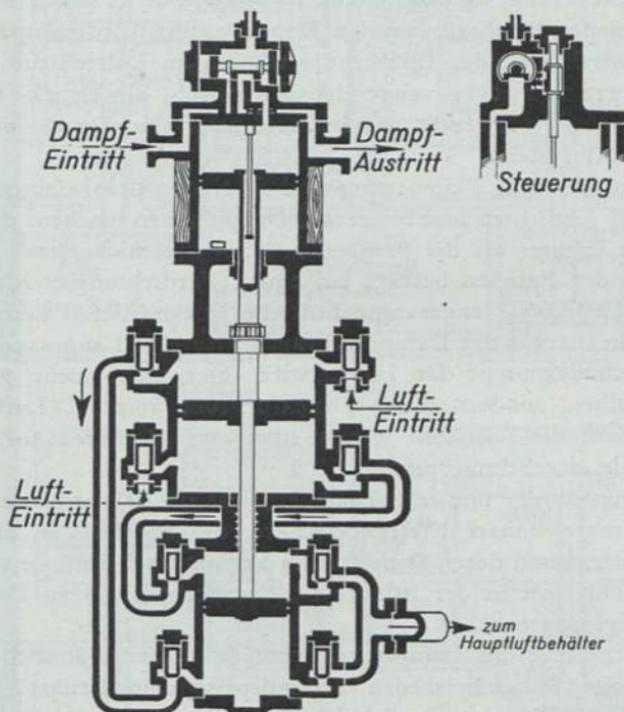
Zweistufige Luftpumpe mit Schlepfschiebersteuerung
